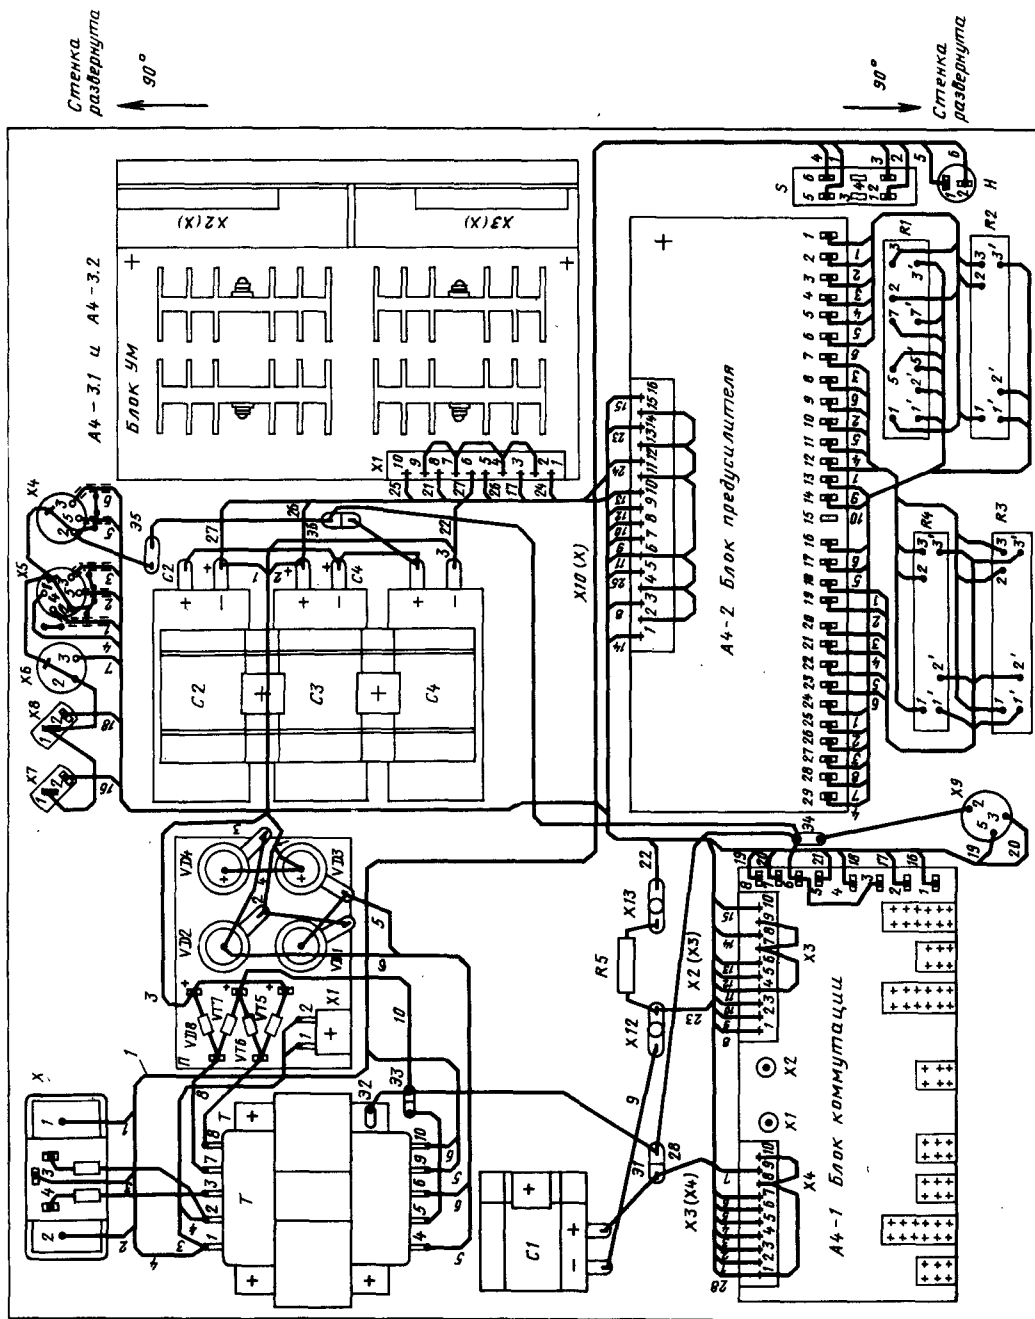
Электромонтажная схема соединений навесного монтажа
